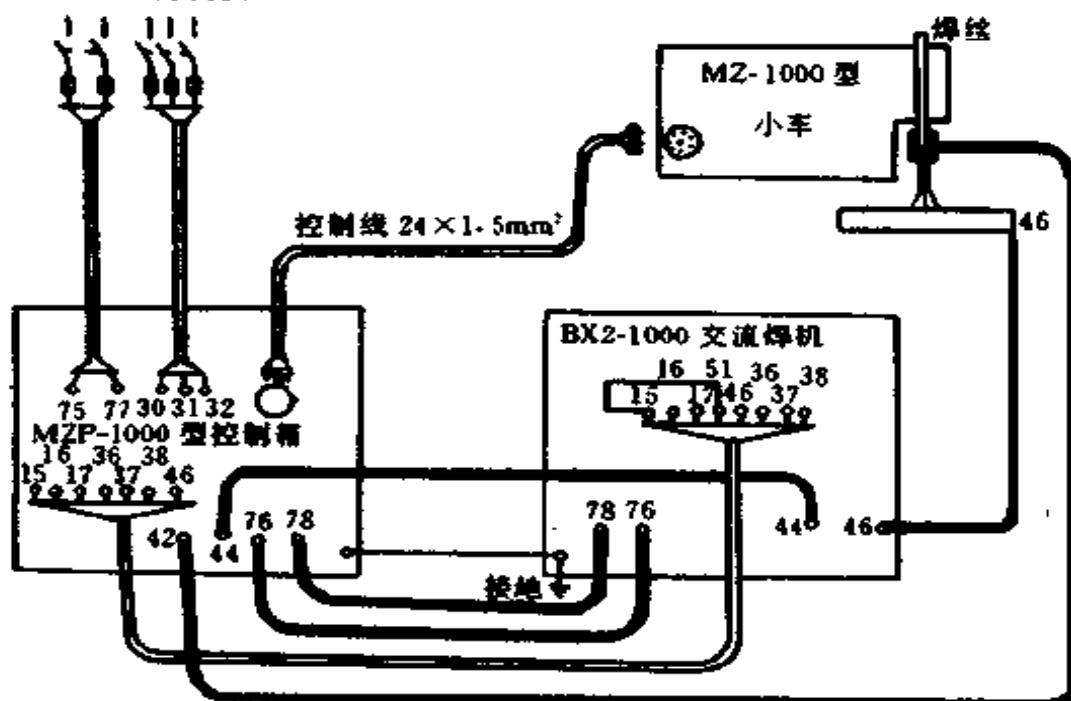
MZ-1000 型焊机外部接线图(交流焊接电源)
